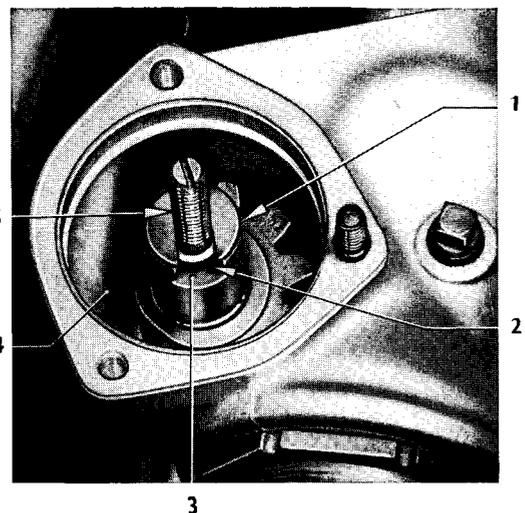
Lenkstockwelle mit Einstellschraube im Lenkgehäuse
